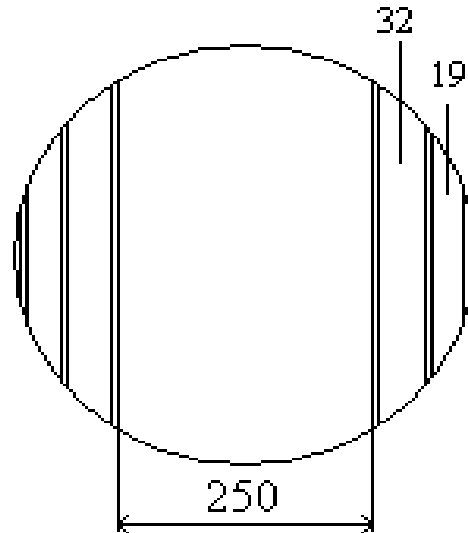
Схема розкрою лісоматеріалу круглого на необрізні пиломатеріали та брус (I прохід)
